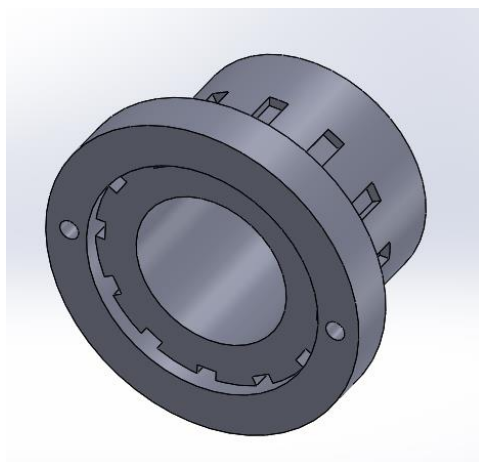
Vista inferior útil rotor (Font: SolidWorks) [14]
